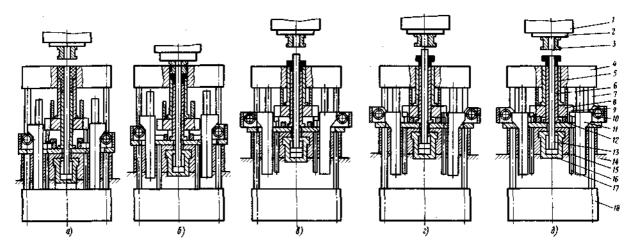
Схема типовой конструкции пресс-блока для прессования втулок с наружным буртом:
